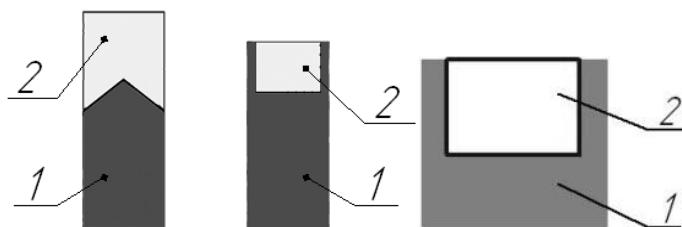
Модели составных заготовок: 1-конструкционная сталь; 2-штамповая сталь
